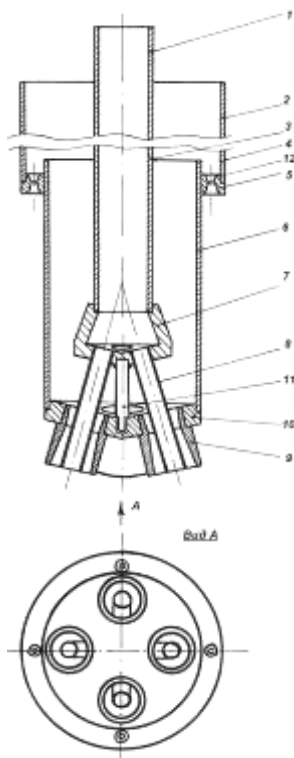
Конструкция двухъярусной гарнисажной газоохлаждаемой газопорошковой фурмы для раздувки шлаковой ванны газовыми или газопорошковыми струями. Обозначения в тексте
